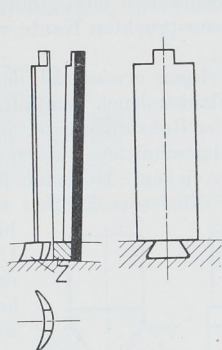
Schaufelbefestigung mittels Schwalbenschwanzes.
